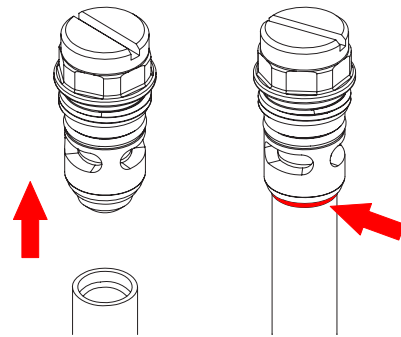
Rimozione del tubo dagli attacchi di accesso.
